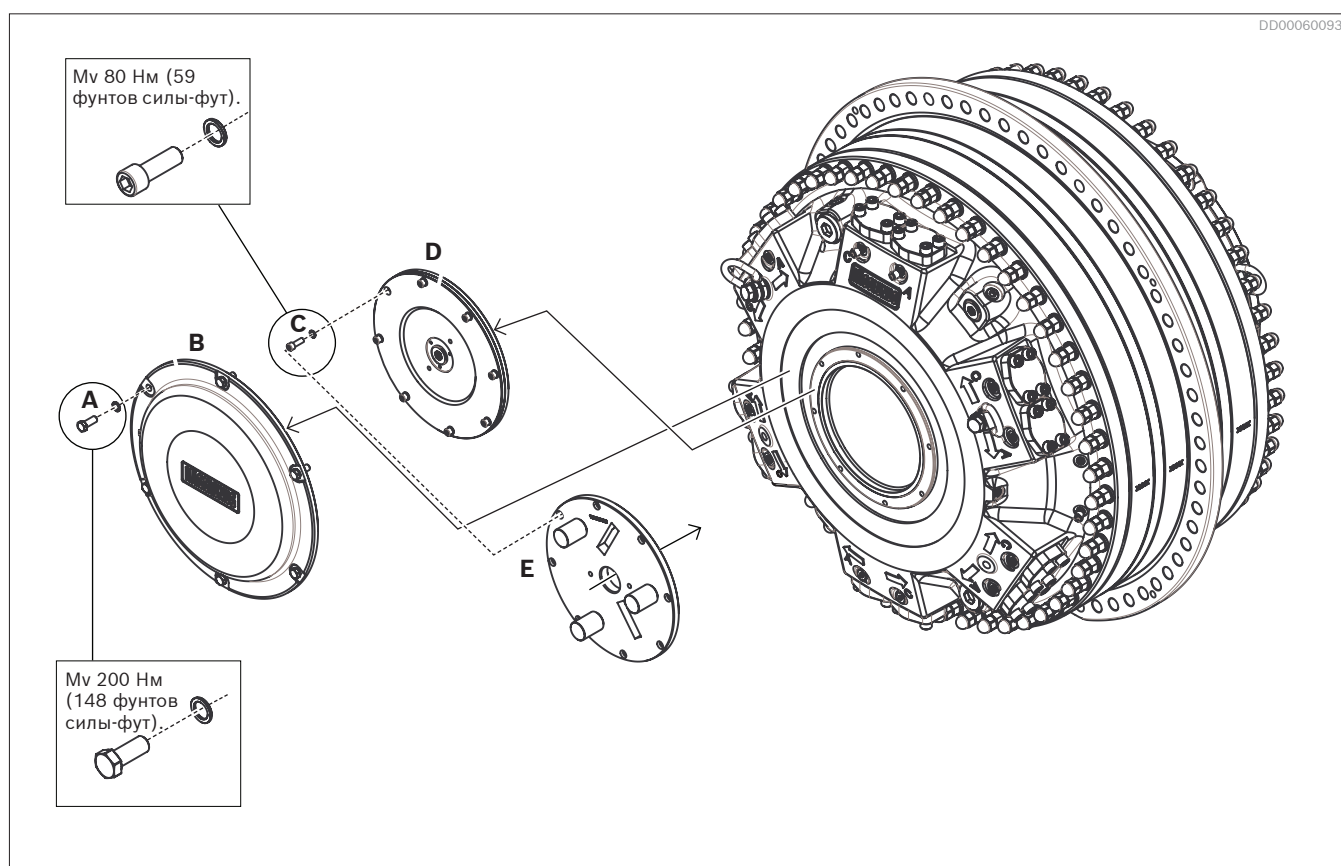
Установка инструмента для совмещения зубьев и пазов шлицевого соединения
